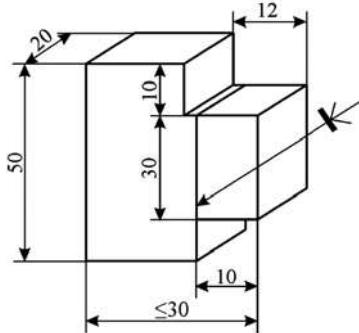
Форма та розміри склесних зразків деревини дуба / Shape and dimensions of bonded oakwood samples
